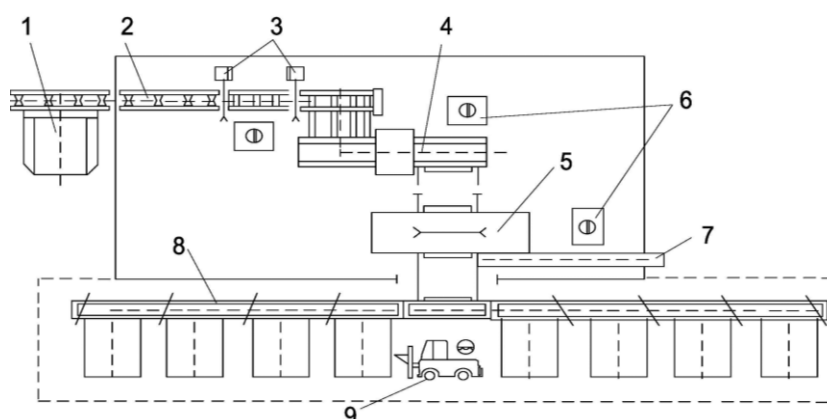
Технологическая схема шпалопильного цеха с применением станка для чистой окорки: 1 – питатель буферный; 2 – конвейер роликовый; 3 – установка раскряжевочная; 4 – станок окорочный; 5 – шпалоавтомат; 6 – кабина оператора; 7 – конвейер ленточный; 8 – линия сортировки и пакетирования шпал; 9 – автопогрузчик
